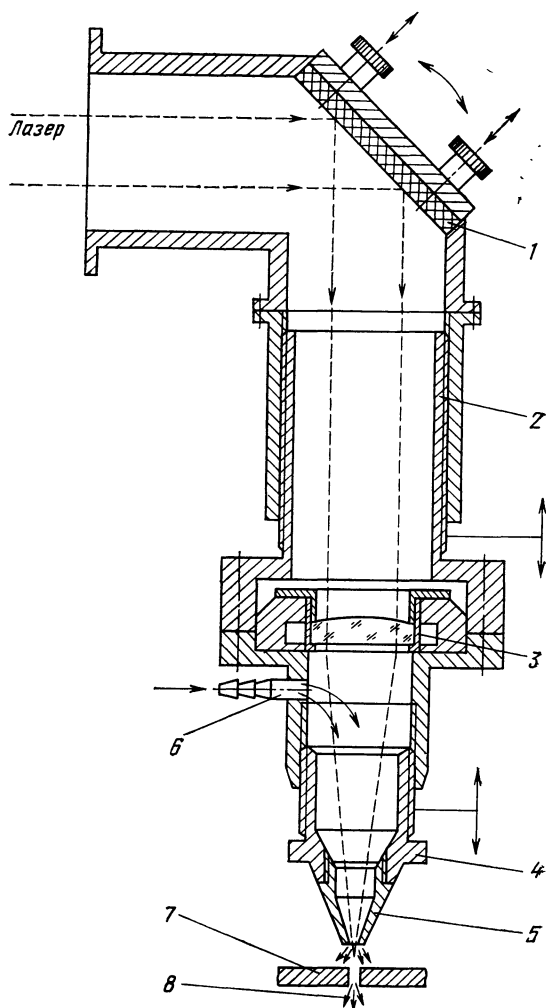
Обрабатывающая головка для CO_2 -лазера с подачей струи газа:
